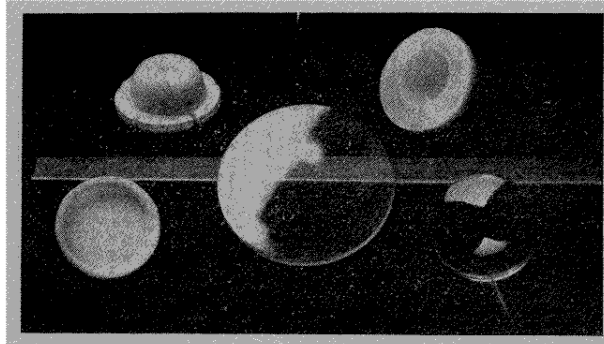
Vue de pièces en silice estampées à chaud : bornes de condensateur, lentilles, plaque transparente de 100 mm de diamètre.
